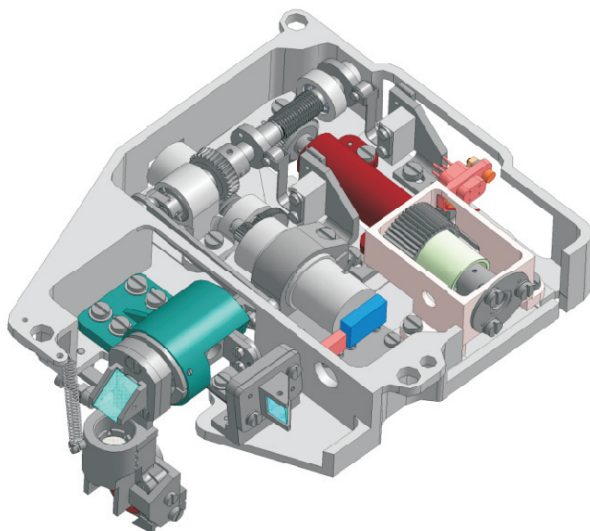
3D-прототип под сборки узла мехатронного прибора
